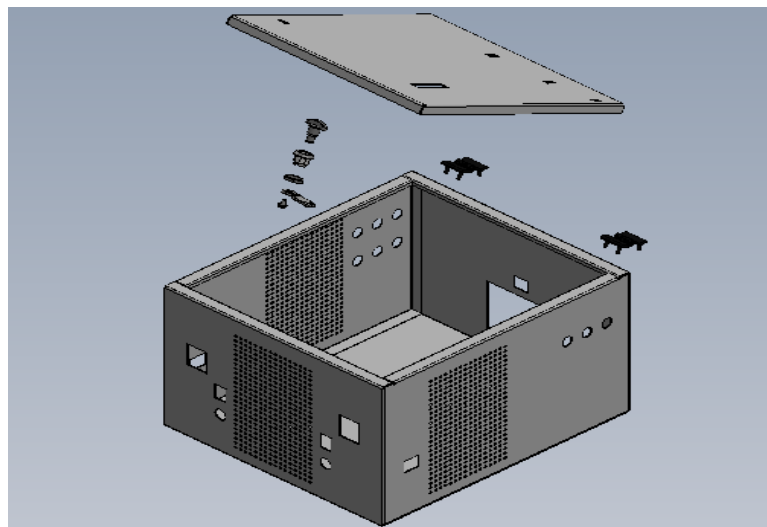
Vista explosionada de diseño de caja o gabinete. Fuente Autores.
